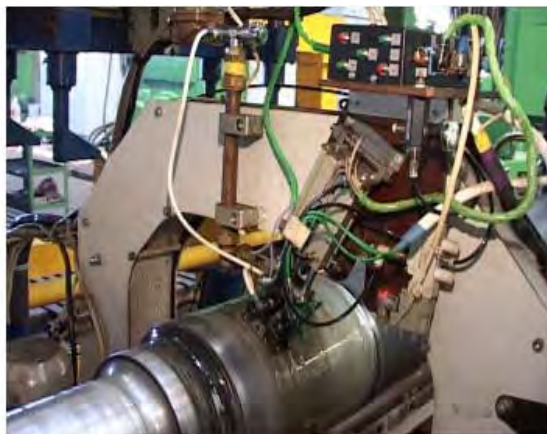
Установка для контактного ультразвукового контроля объема металла заготовок железнодорожных осей
